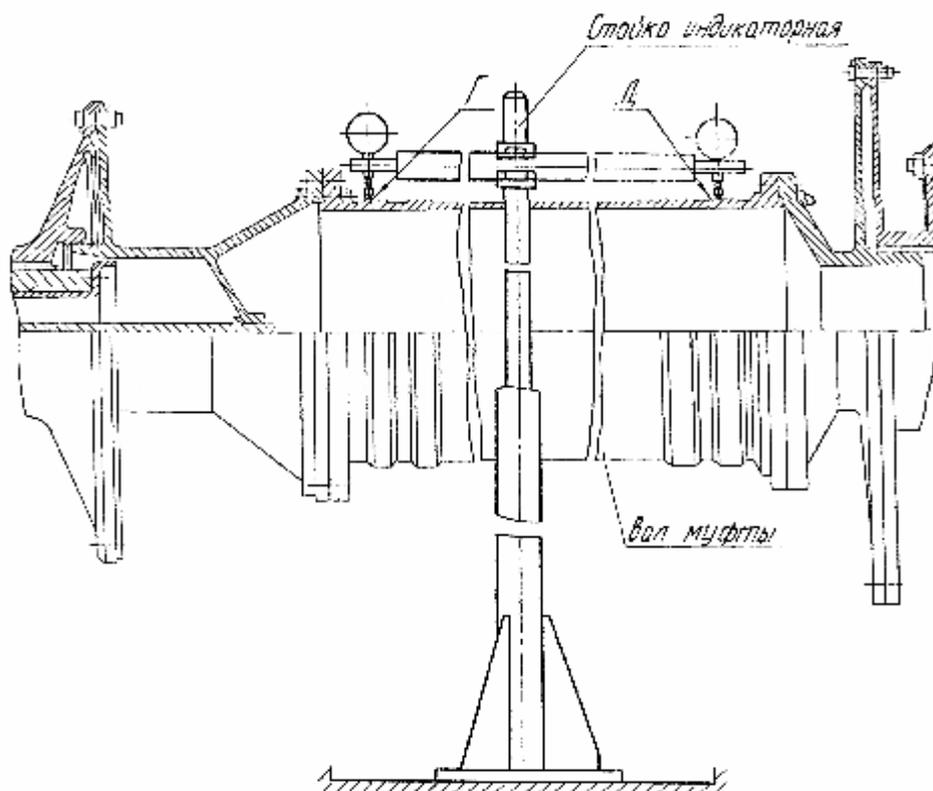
Установка индикаторной стойки для контроля биений на валу муфты
